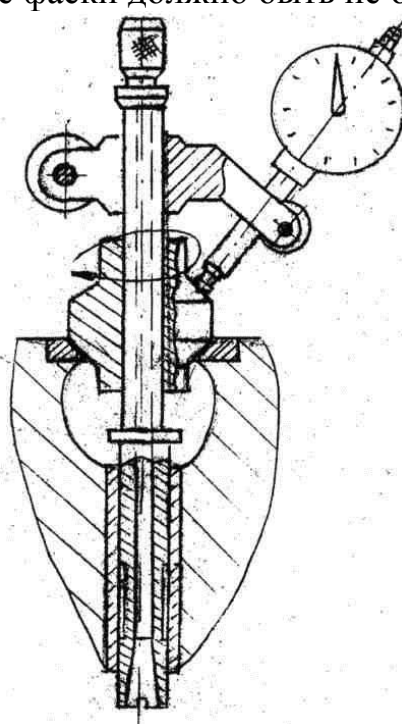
Индикаторное приспособление для контроля соосности
